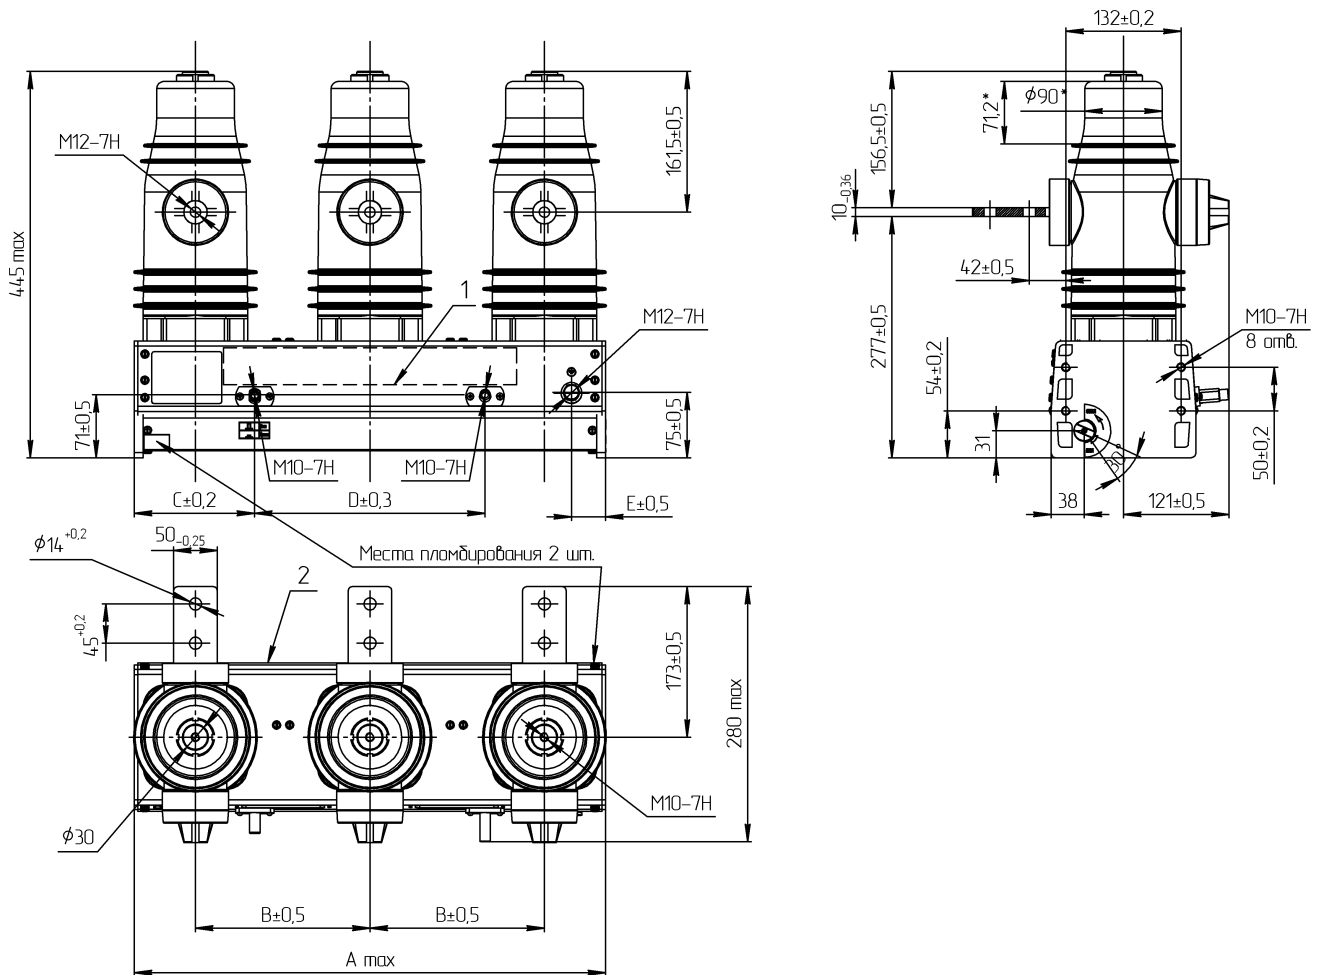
Габаритные, установочные и присоединительные размеры ВВ конструктивного исполнения 7 (остальное см. рис. рис.А.1 и А.2)
